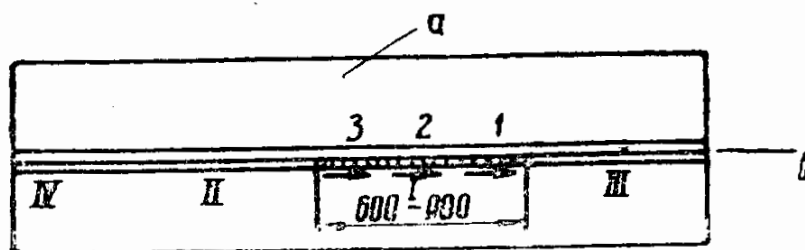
Порядок сварки и размер секции при многослойной сварке угловых швов: *a* — лист полки; *b* — лист стенки; 1, 2, 3 — порядок наложения швов; I, II, III, и IV — номера секций (стрелками указано направление сварки).
